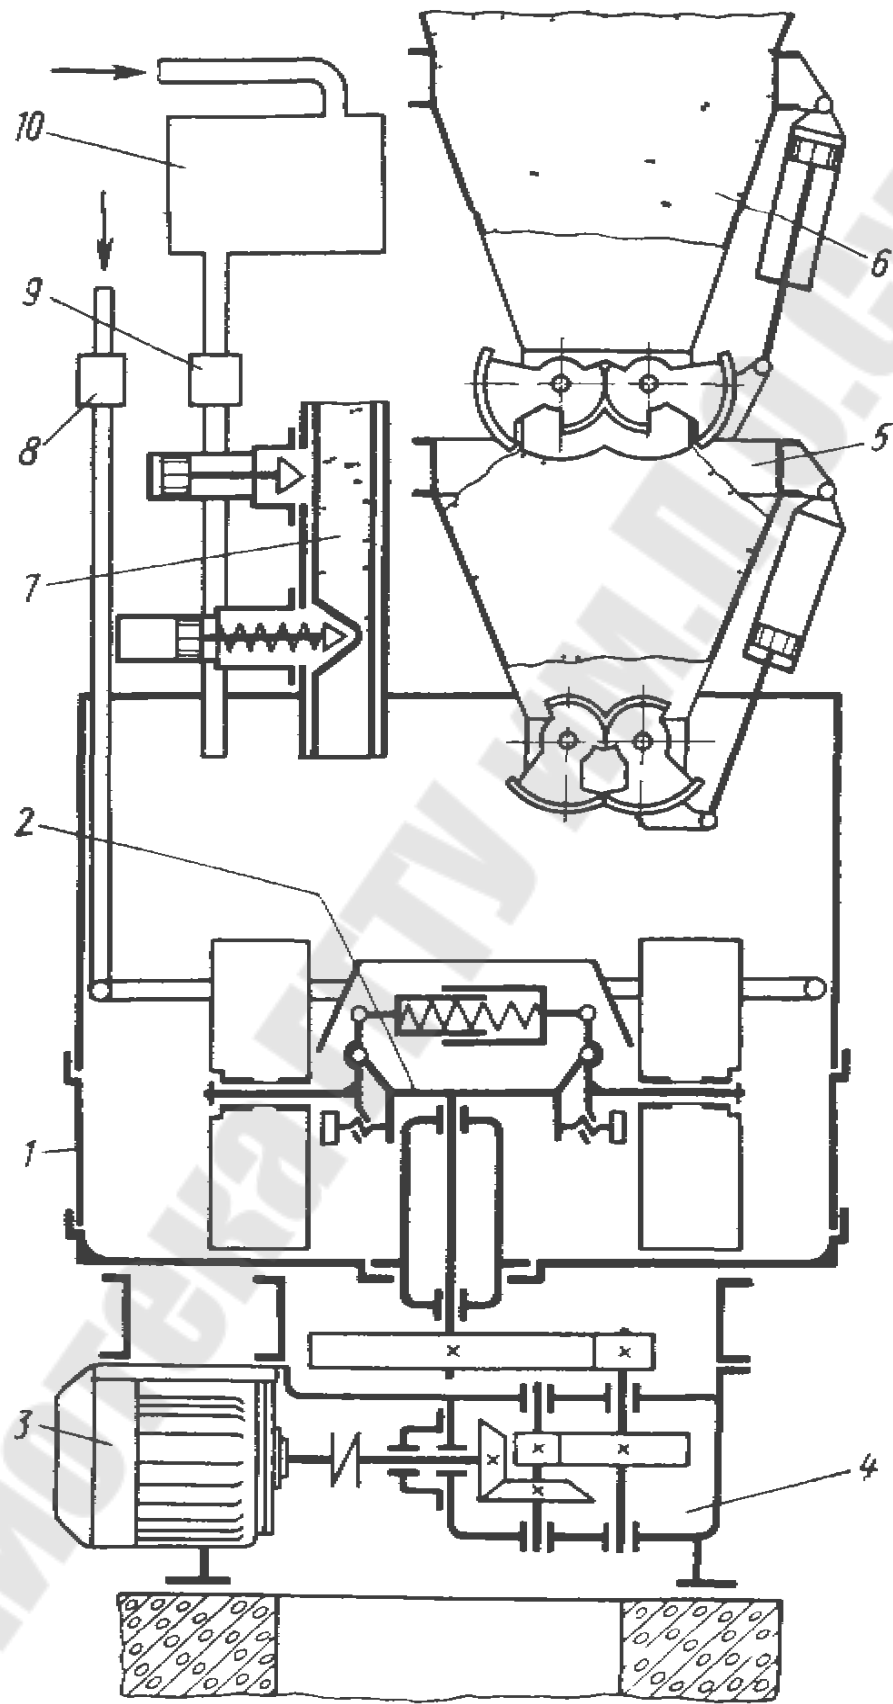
Схема установки для приготовления единой формовочной смеси
